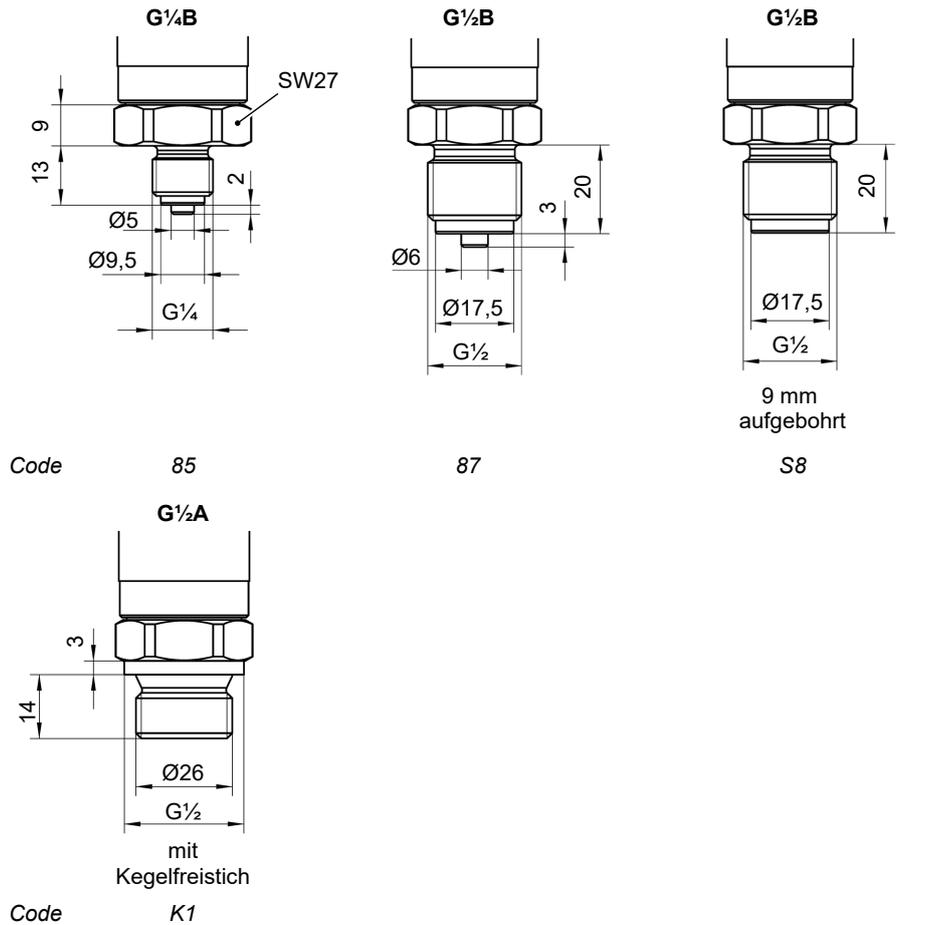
Prozessanschlüsse mit zölligem Gewinde
